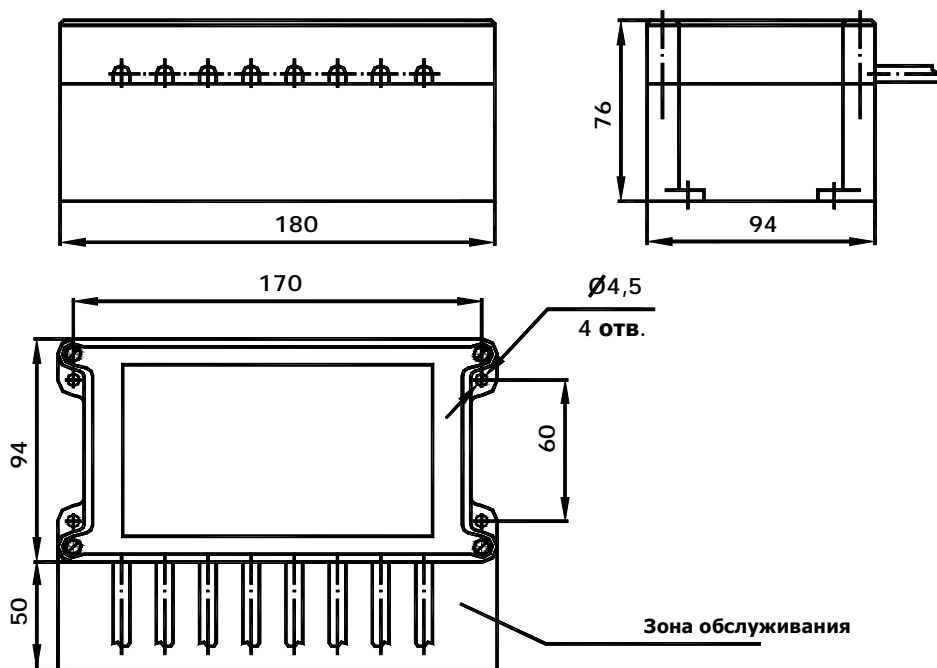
Габаритный чертеж блока питания ИПС.
